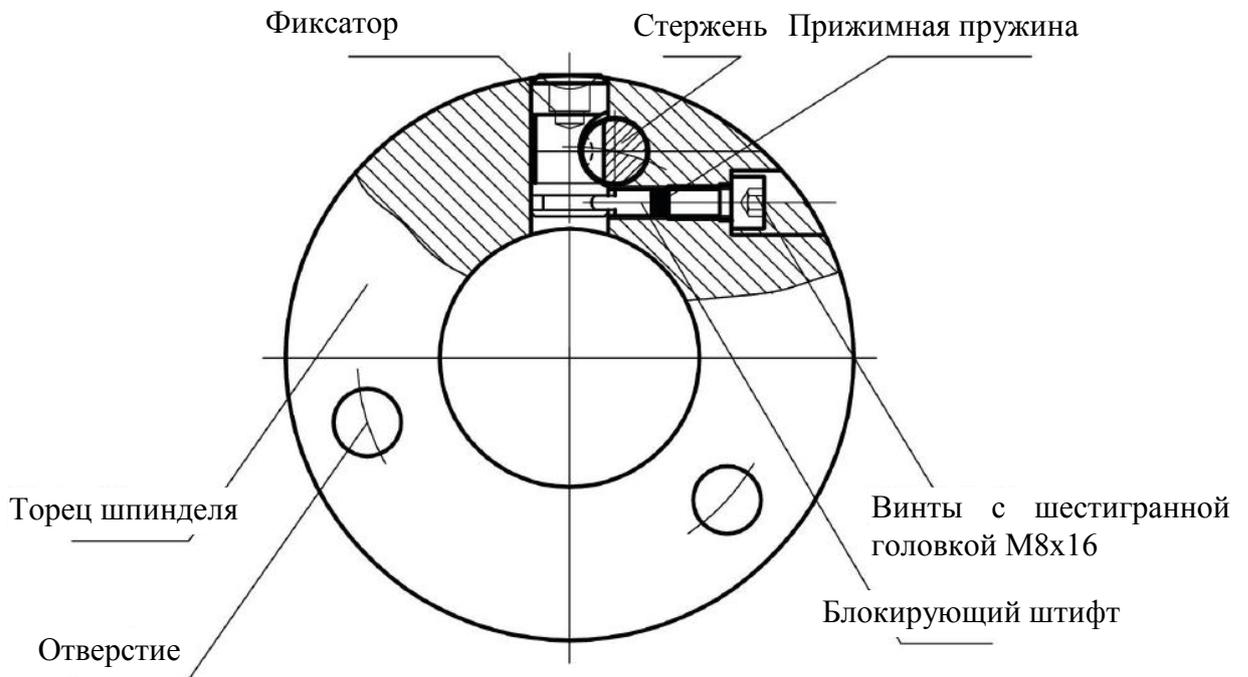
Конструкция блокировки патрона или торцевой пластины
